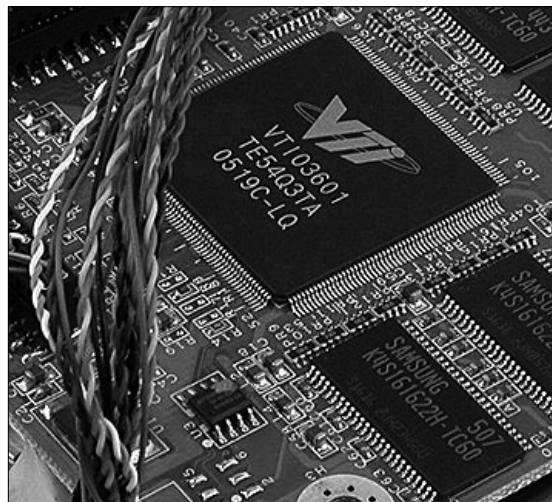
PCB上编号为VT103601的芯片就是Overdrive主控芯片
